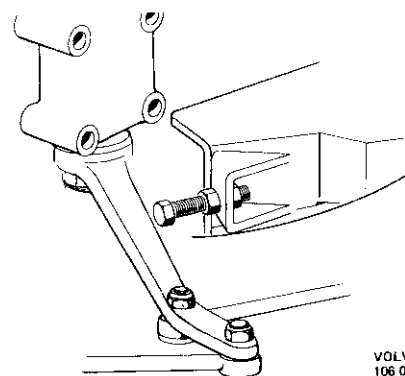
Stellbare Anschlagsschraube für Lenkbegrenzung
